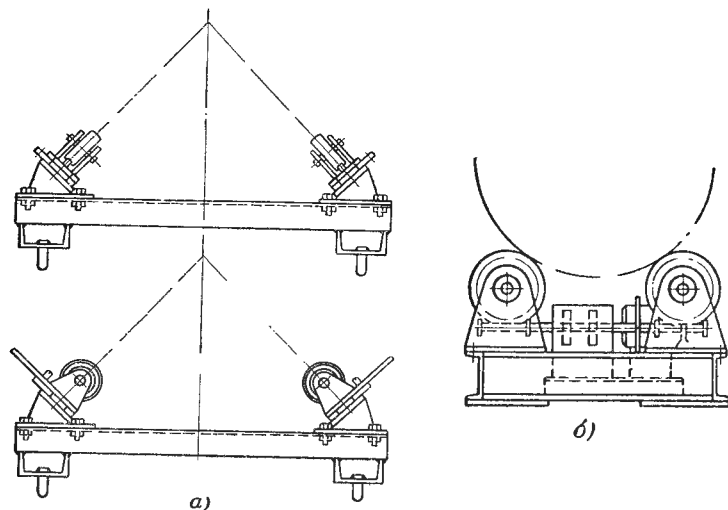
Роликовые кантователи для сборки и сварки цилиндрических обечаек.
